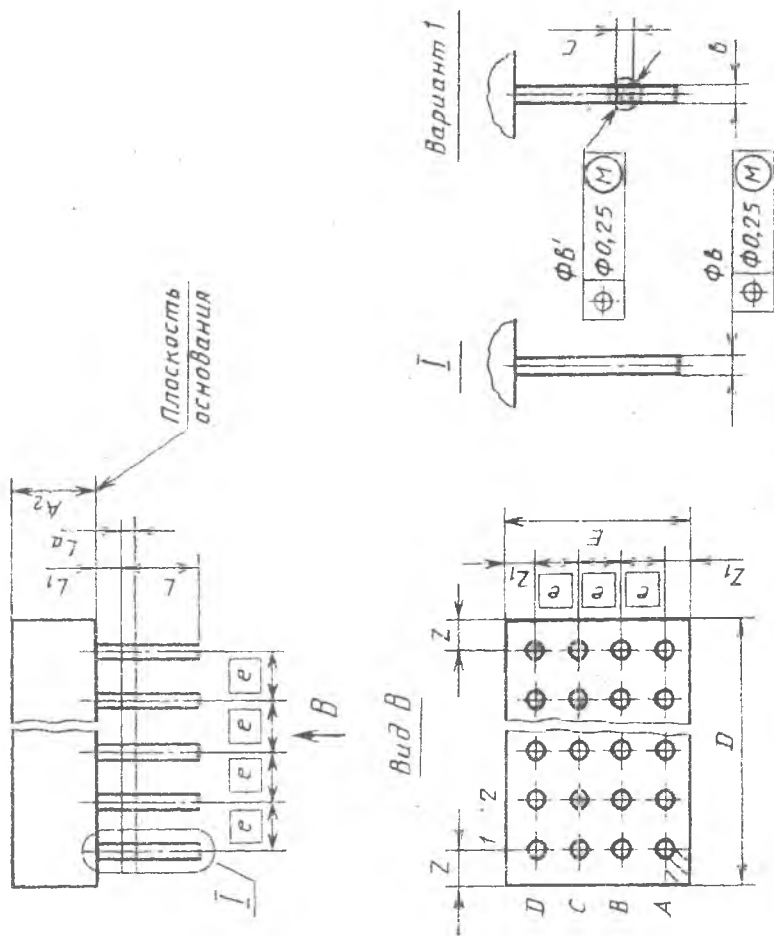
Конструкция корпуса типа 1 подтипа 3
